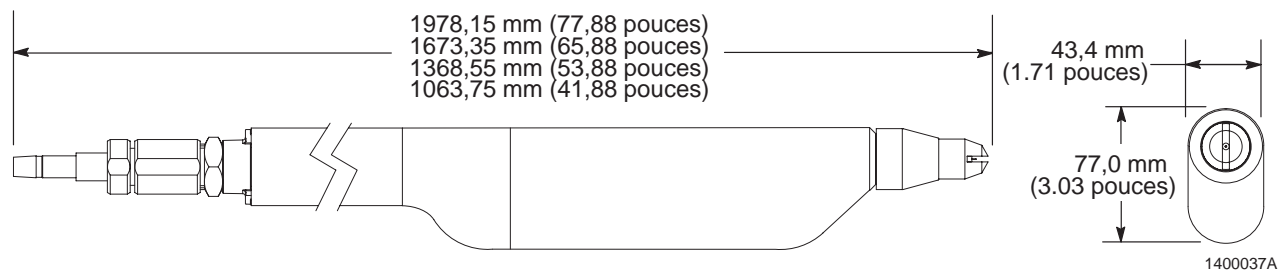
Dimensions du pistolet de poudrage automatique Sure Coat à fixation par tube
